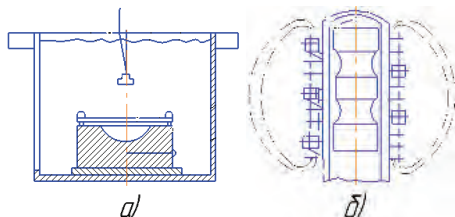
Штамповка взрывом (а) и электромагнитная штамповка (б)
